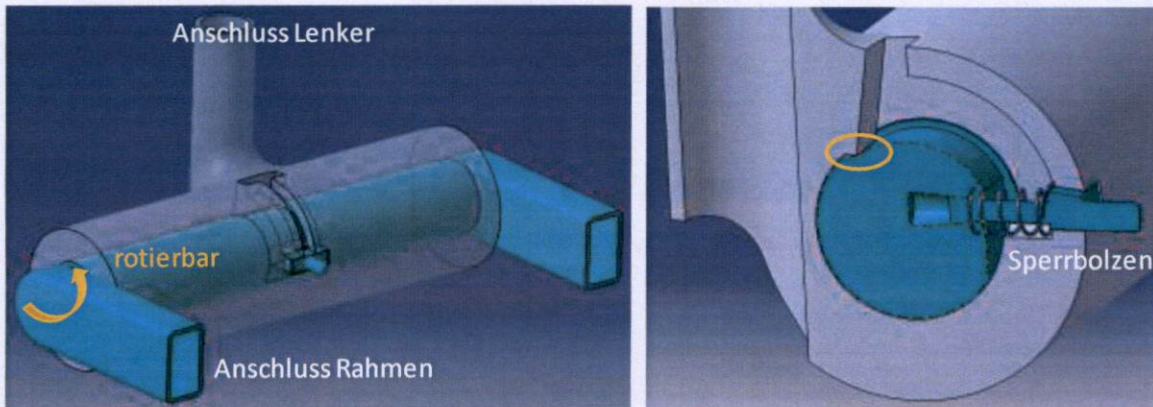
Zylindergelenk mit mechanischem Sperrbolzen
